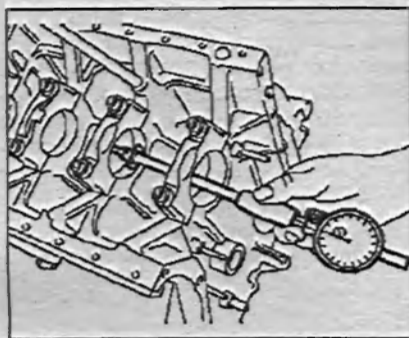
Измерение диаметров отверстий под коренные подшипники коленчатого вала.
